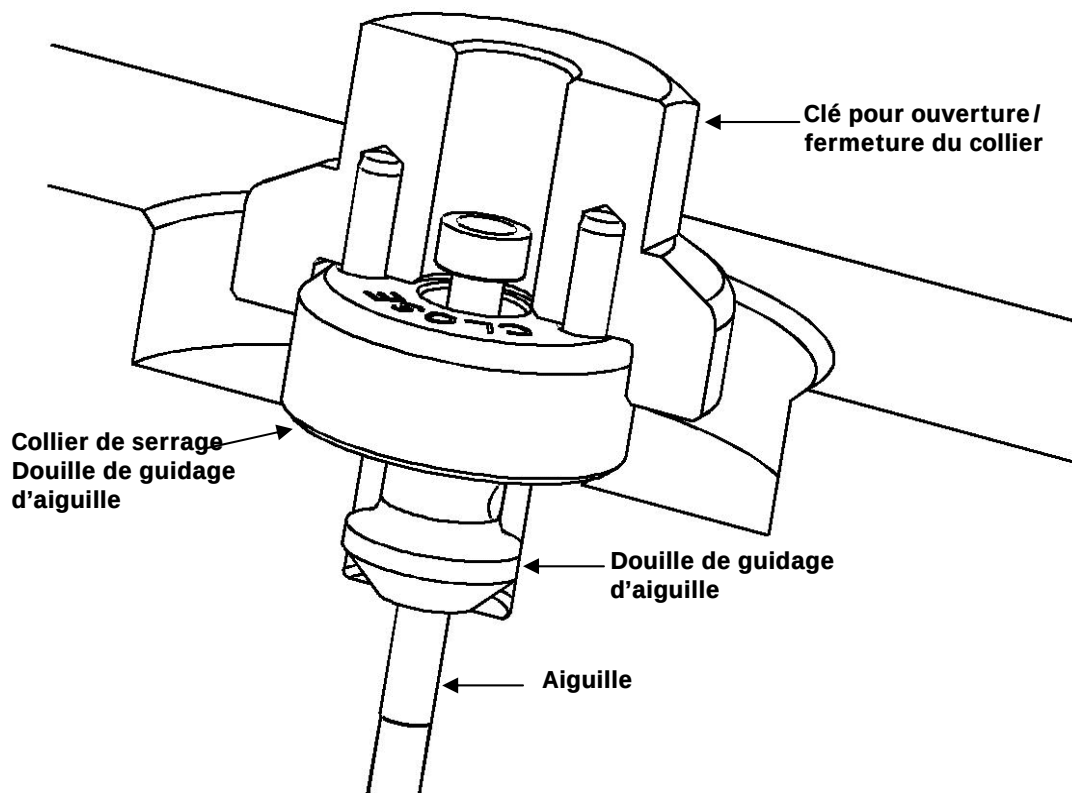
Assemblage du collier de serrage de la douille de guidage d'aiguille
